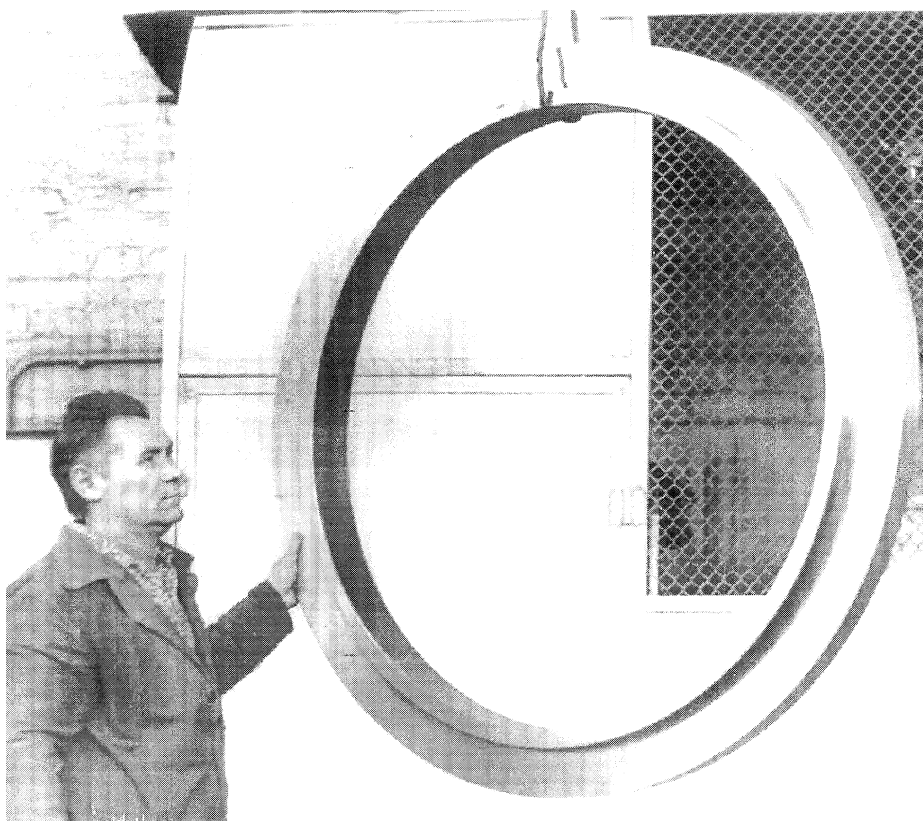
Жорстке зубчасте колесо хвильового редуктора приводу повороту рудорозмельного млина МГР 5500 × 7500
